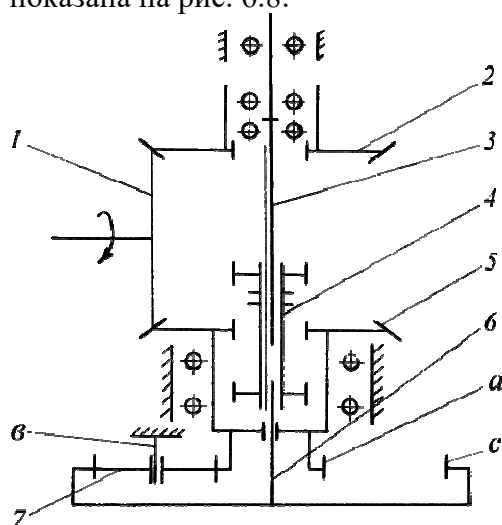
Схема планетарного ходозменшувача, вбудованого в коробку передач з поперечними валами
